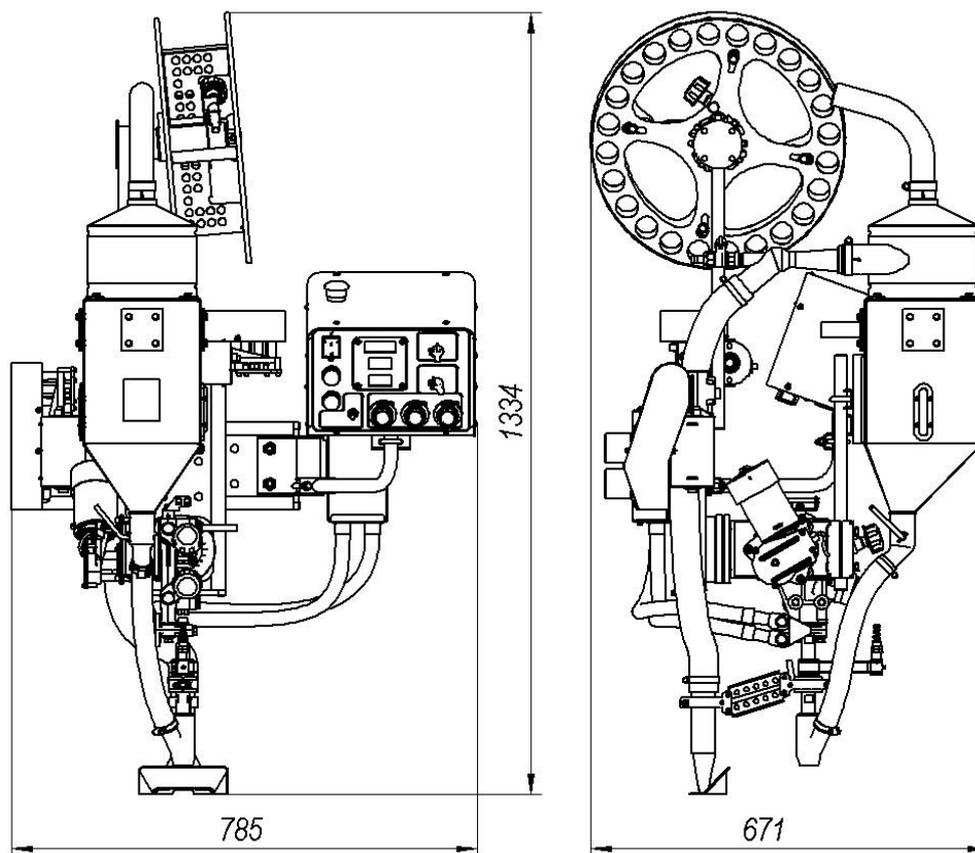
Автомат сварочный АДФ-1000 сер.06 исп.05.
